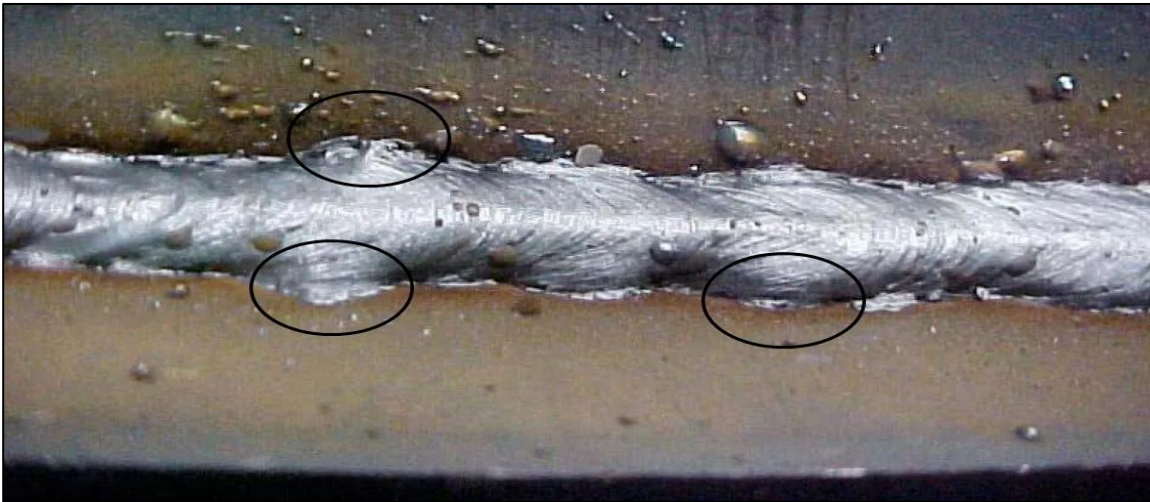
Traslape o Traslapo En Soldadura [48].
